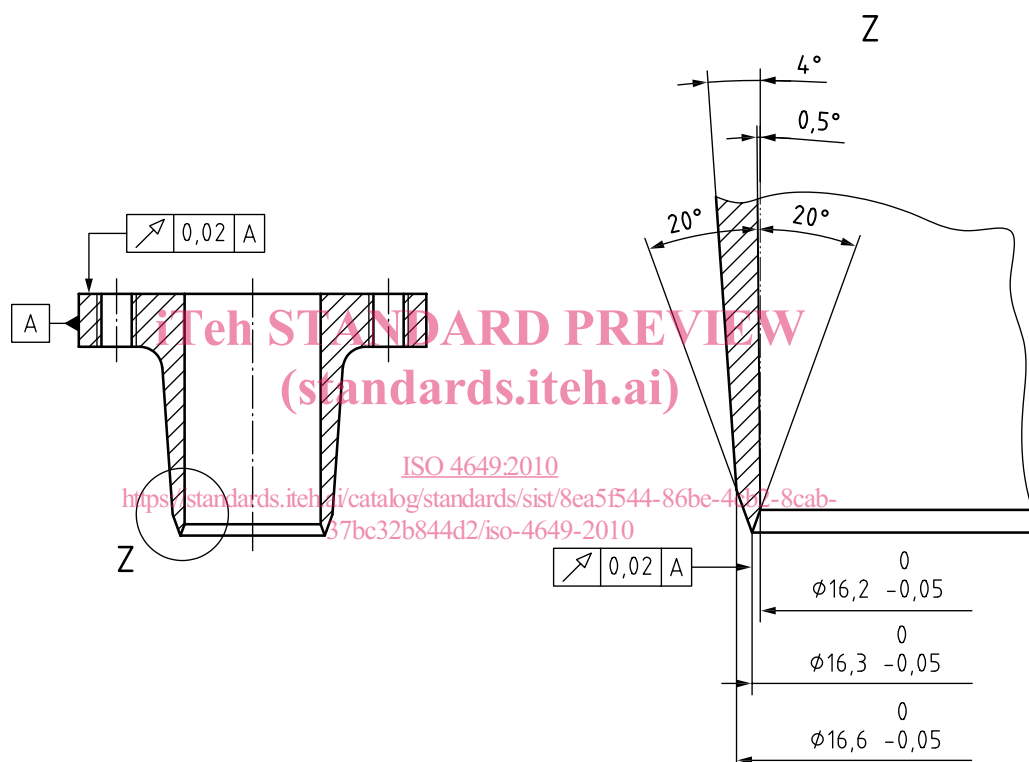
Exemple d'emporte-pièce rotatif pour la préparation d'éprouvettes
